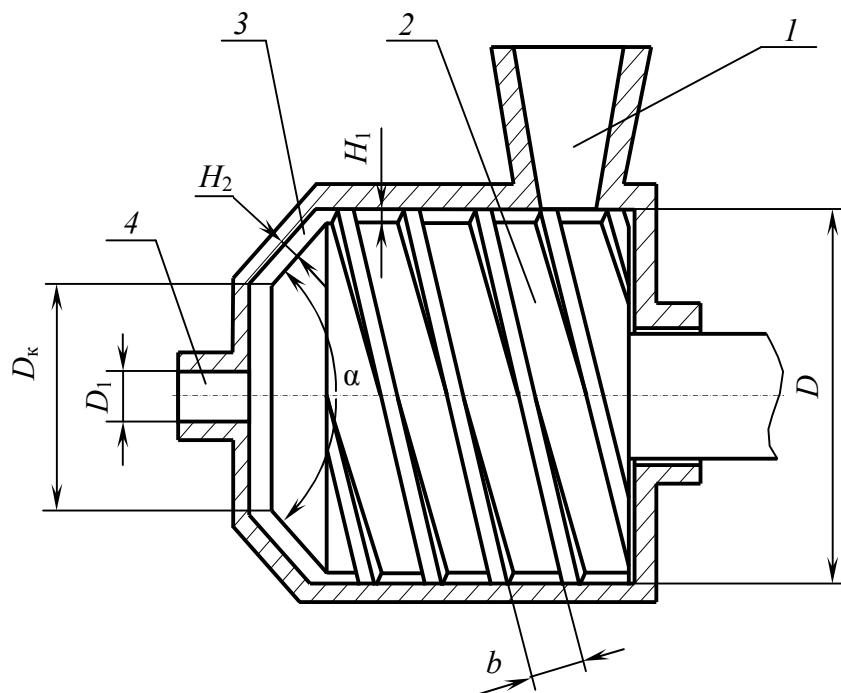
Принципова схема дискового розплавлювача: 1 – завантажувальний отвір; 2 – диск; 3 – дисковий зазор; 5 – центральний випускний отвір корпусу; D , D_1 , D_k – діаметр внутрішньої поверхні корпусу, центрального випускного отвору корпусу та торцевої частини диска, відповідно, м; b , H_1 – ширина і глибина гвинтової нарізки циліндричної частини диска, відповідно, м; H_2 – величина дискового зазору, м; α – кут конічної частини диска, ...°
